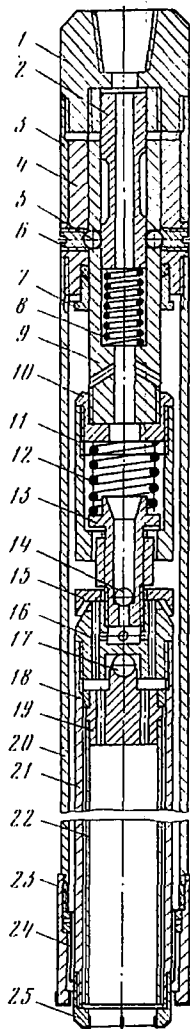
Двойной колонковый снаряд ДКС-3 конструкции А. А. Гребенюка.
